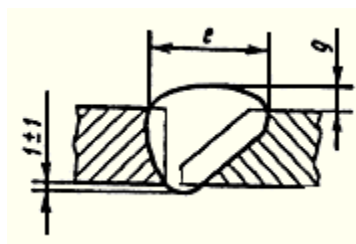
Конструктивные элементы сварного шва соединения С8 по ГОСТ 14771-76.
